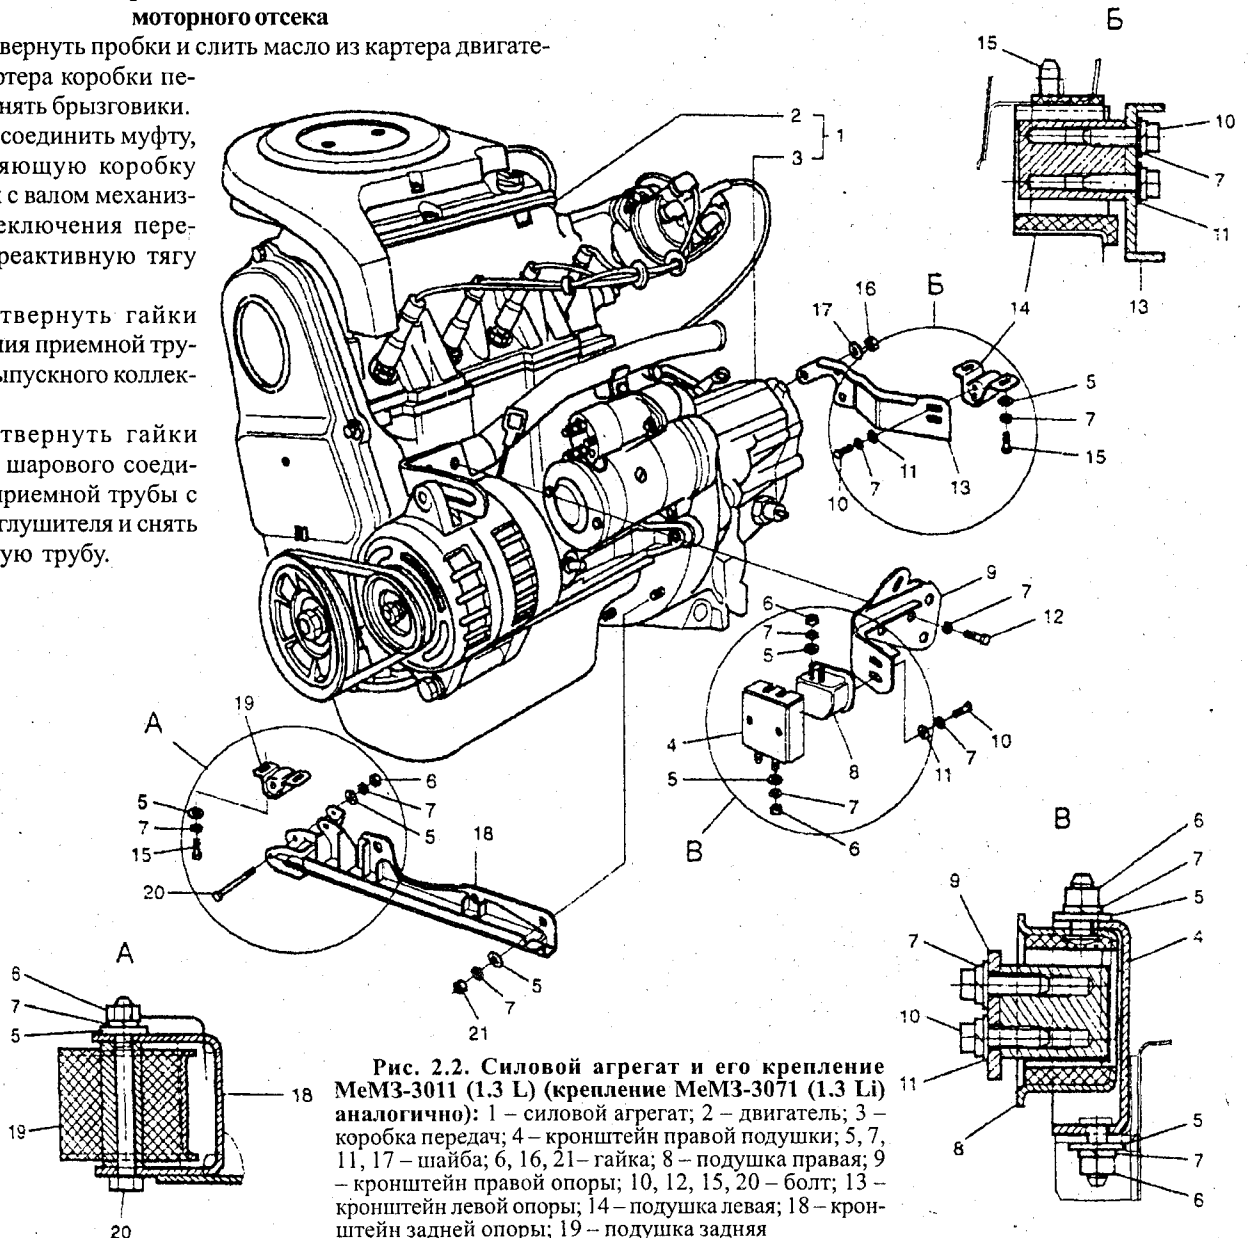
Силовой агрегат и его крепление МеМЗ-3011 (1.3 L) (крепление МеМЗ-3071 (1.3 L) аналогично): 1 – силовой агрегат; 2 – двигатель; 3 – коробка передач; 4 – кронштейн правой подушки; 5, 7, 11, 17 – шайба; 6, 16, 21 – гайка; 8 – подушка правая; 9 – кронштейн правой опоры; 10, 12, 15, 20 – болт; 13 – кронштейн левой опоры; 14 – подушка левая; 18 – кронштейн задней опоры; 19 – подушка задняя
